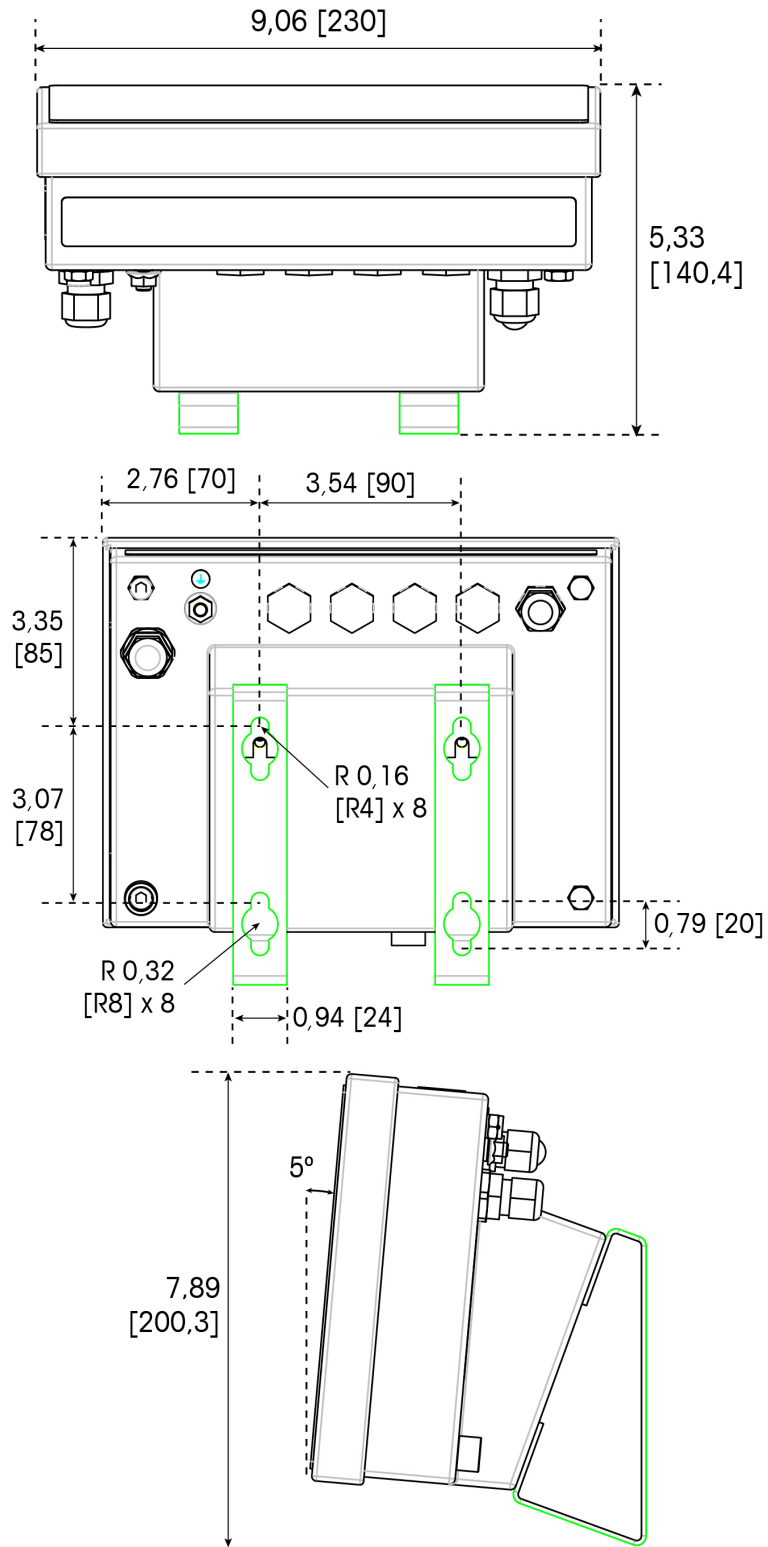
Dimensões IND256x, com suporte fixo de montagem na parede
